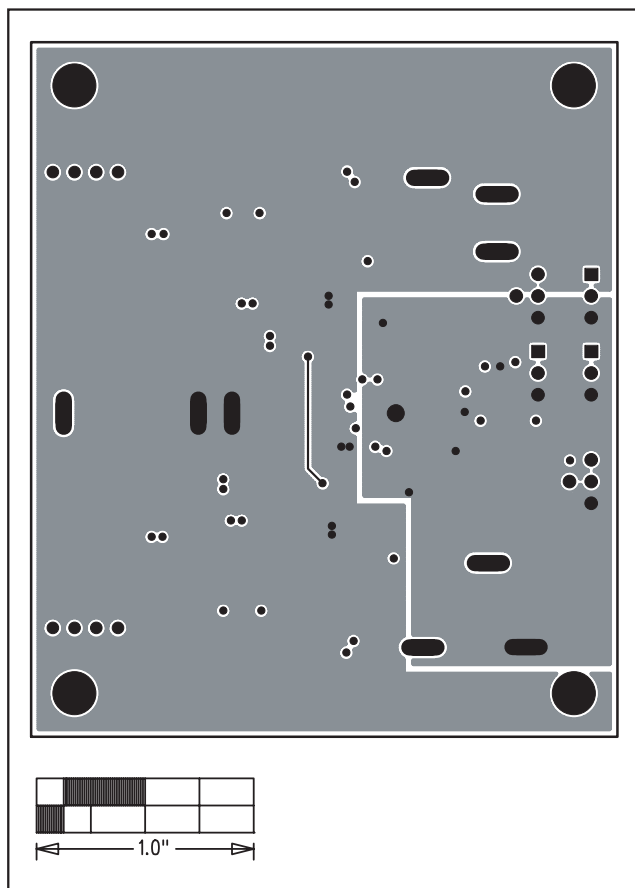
MAX1540 评估板 PCB 布局 – 接地层 3
